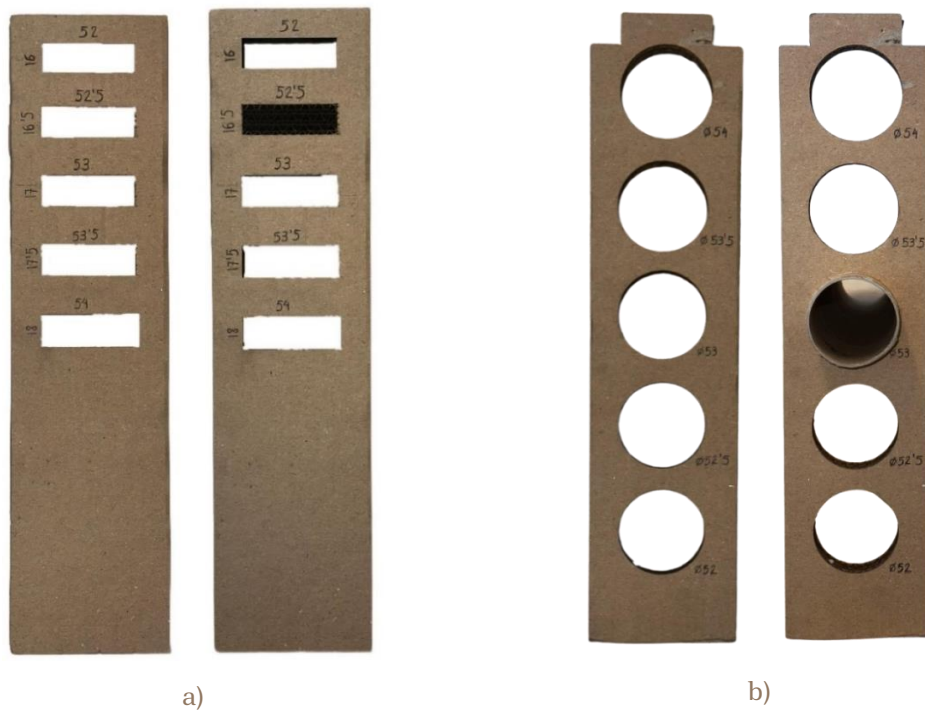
Prueba de tolerancia a) caja y espiga b) elemento tubular || Fuente: Elaboración propia
